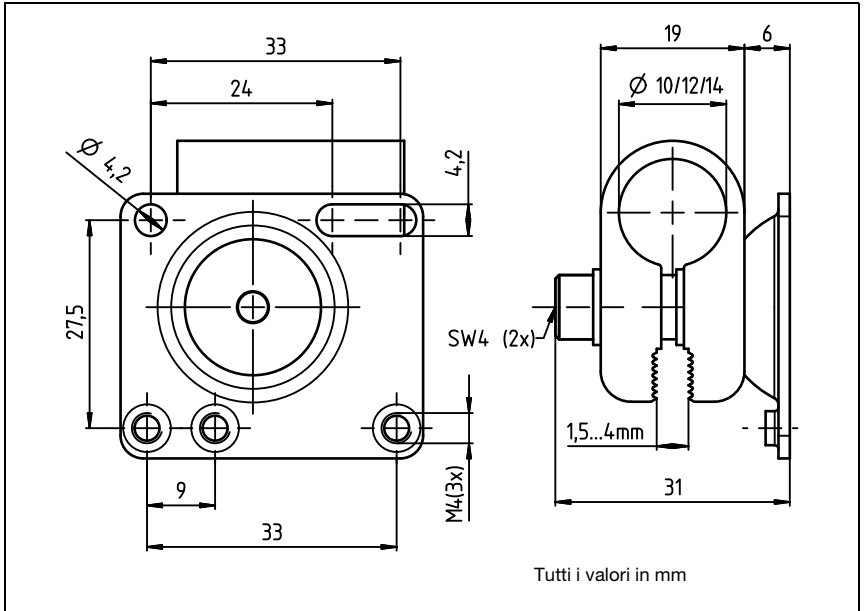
Elemento di fissaggio BTU 300M - D...
